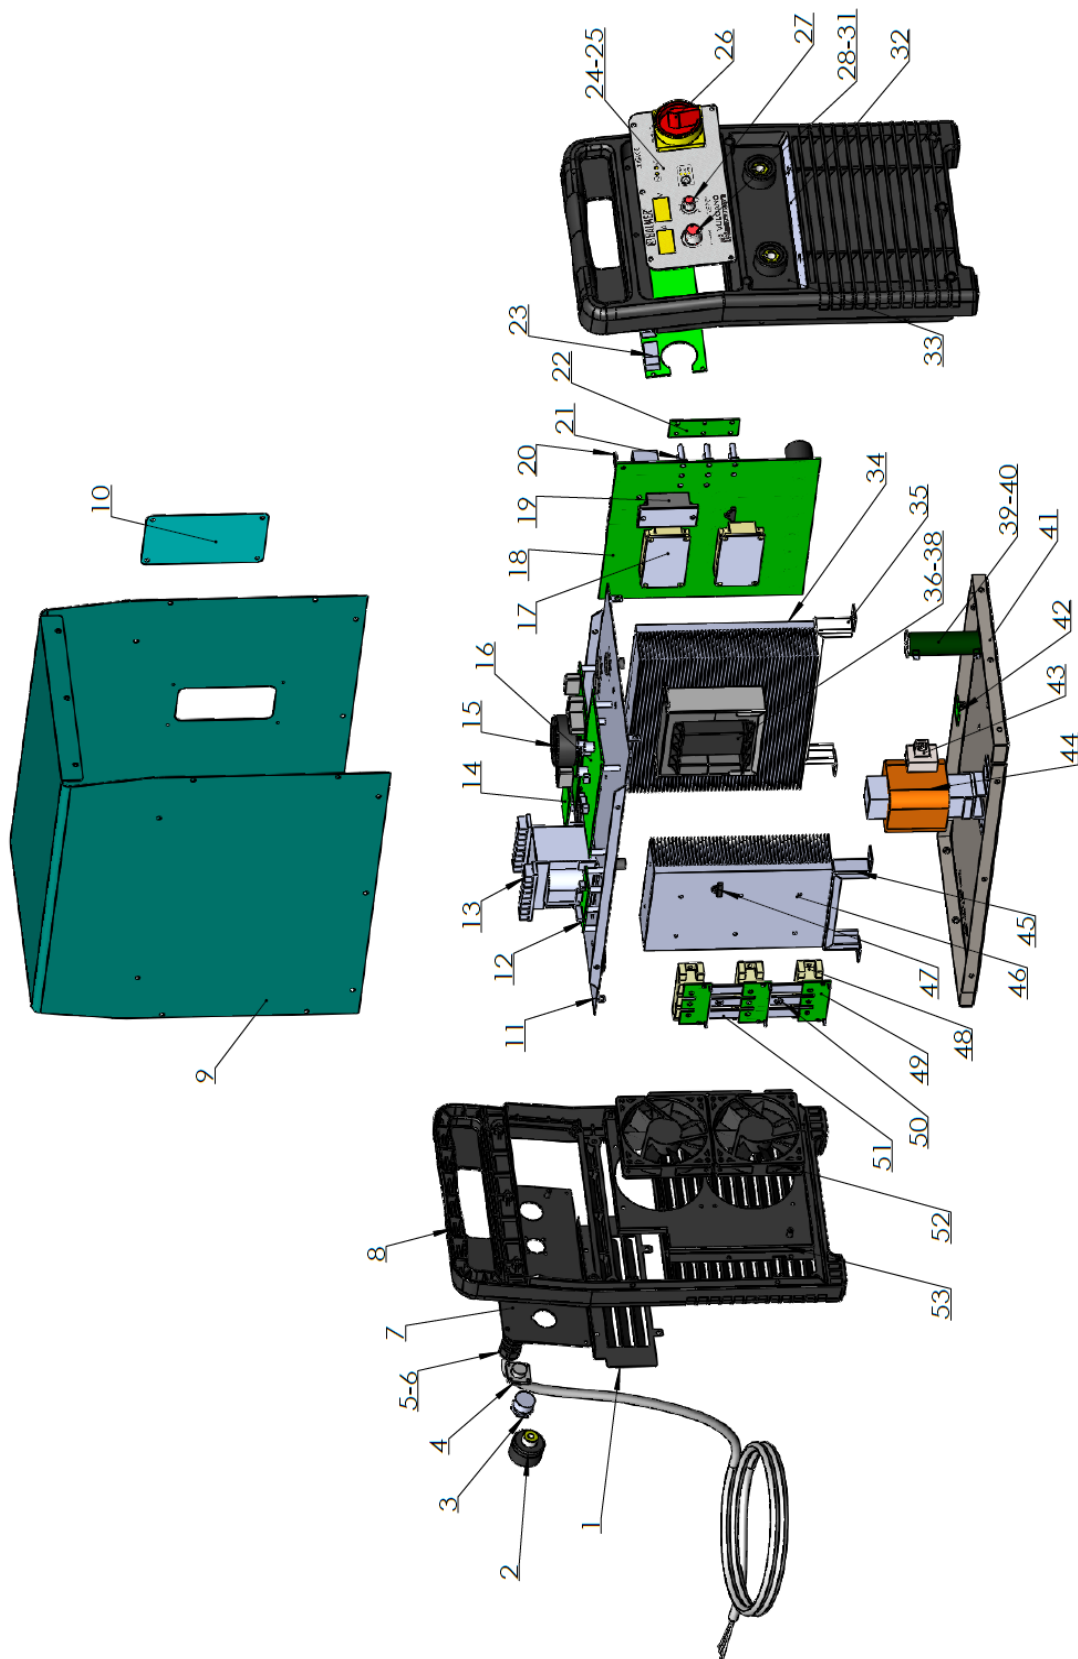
Vista explodida máquina Vulcano Flex MIG 510i.
